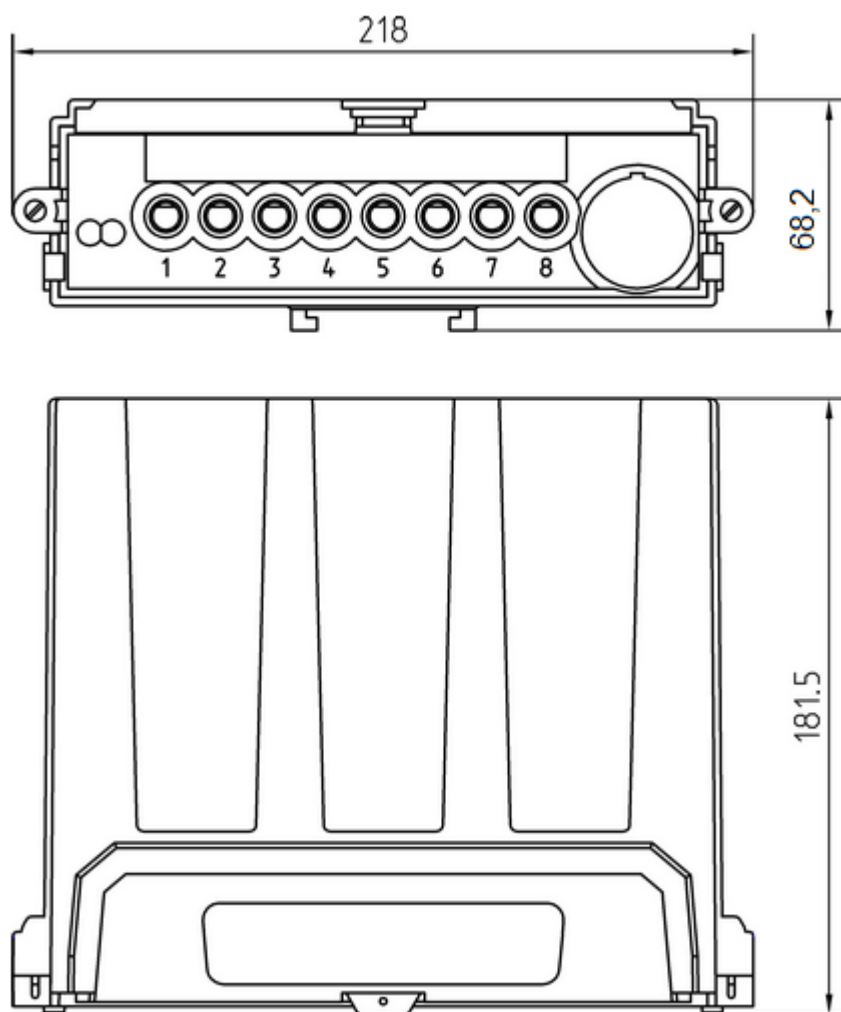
Габаритный чертеж счетчика «Меркурий 238»
